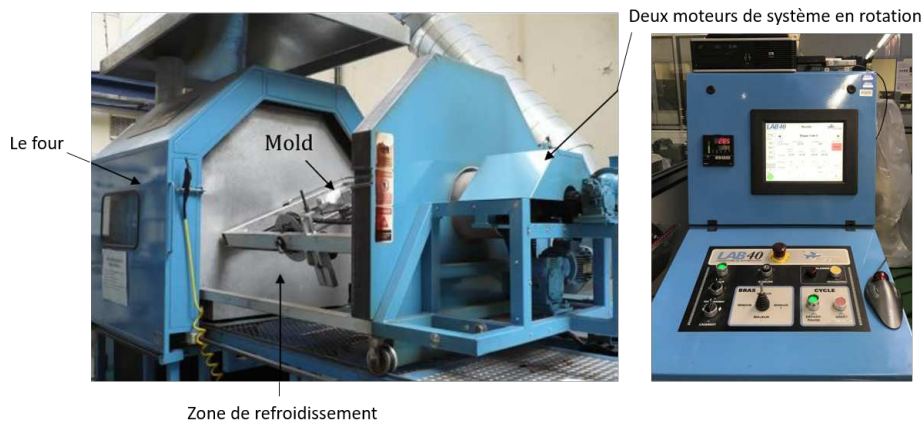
Photographies de la rotomouleuse Lab40 de type Shultle
